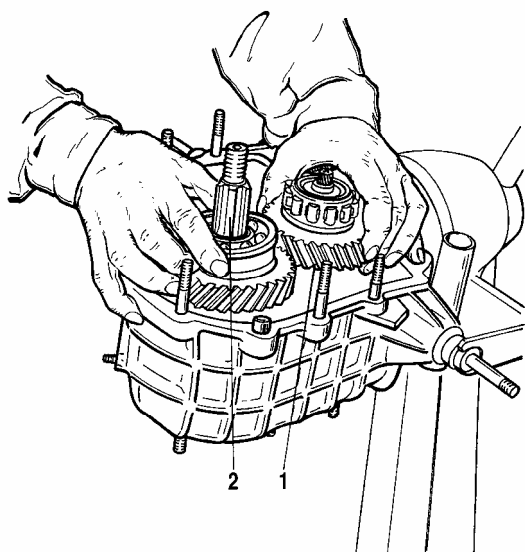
Установка в картер ведущего и промежуточного валов:
